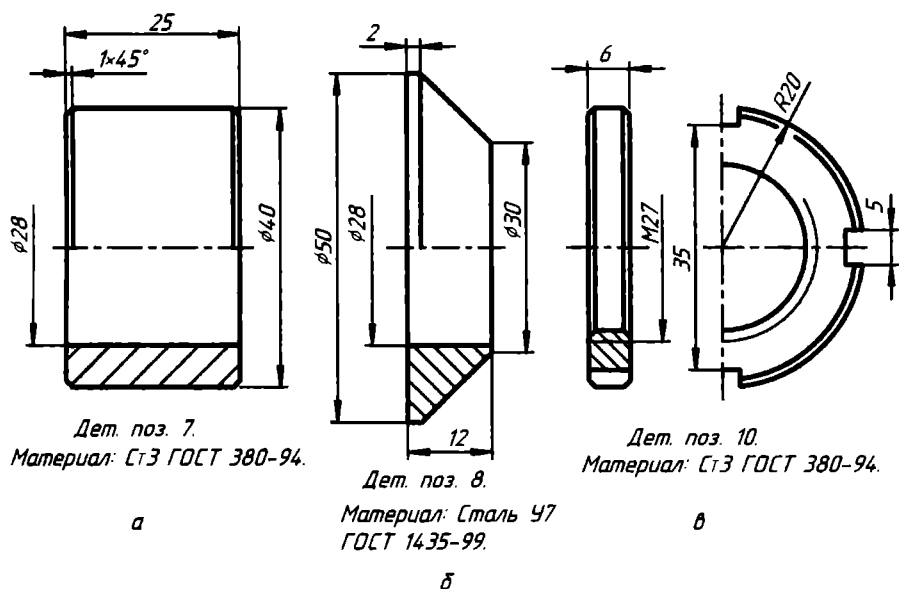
Чертежи: а — втулки; б — конуса; в — гайки
